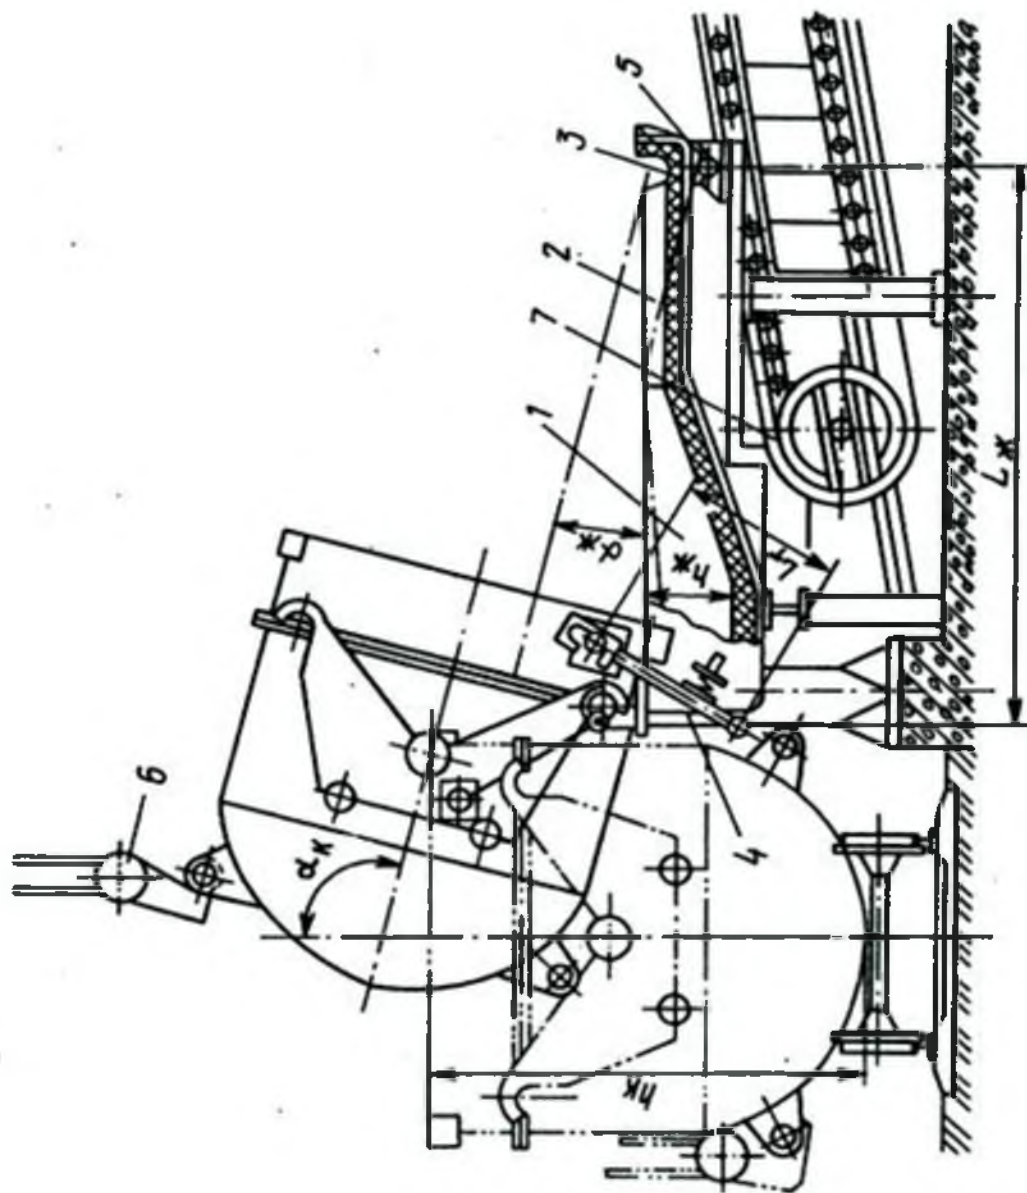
Пристрій для розливки металу із ковша у злитки
